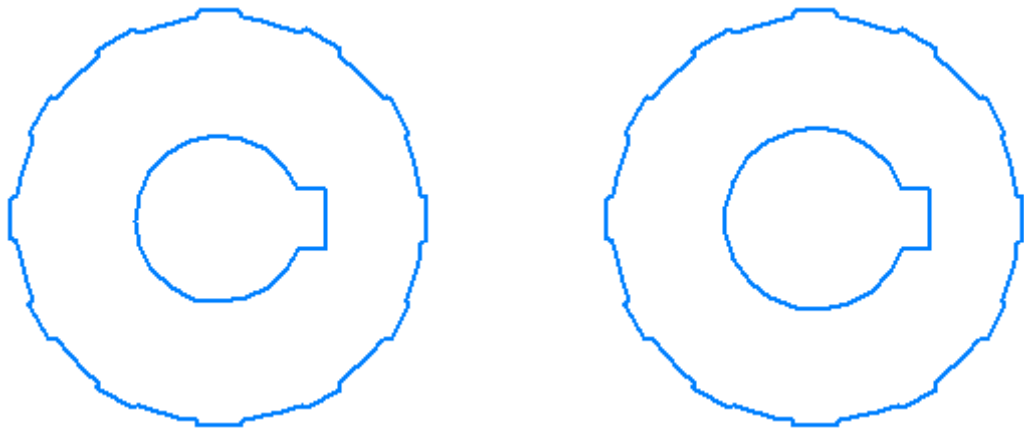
Эскизы, выполненные для изготовления на ЧПУ станке электроэрозионной резки (размеры не приведены)
